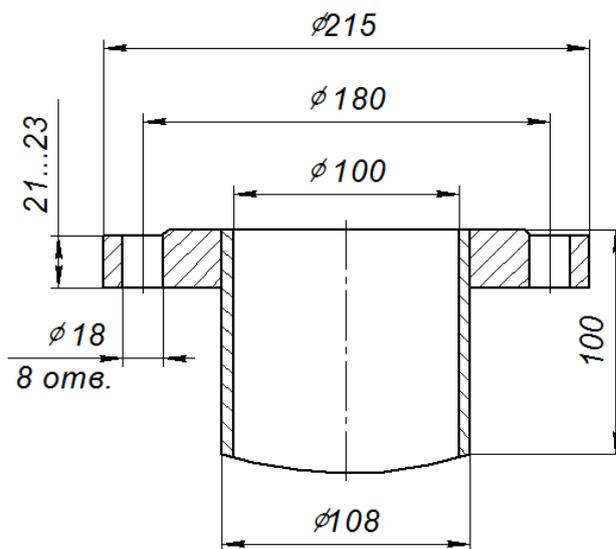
Размеры приварного патрубка на давление до 1,6 МПа
